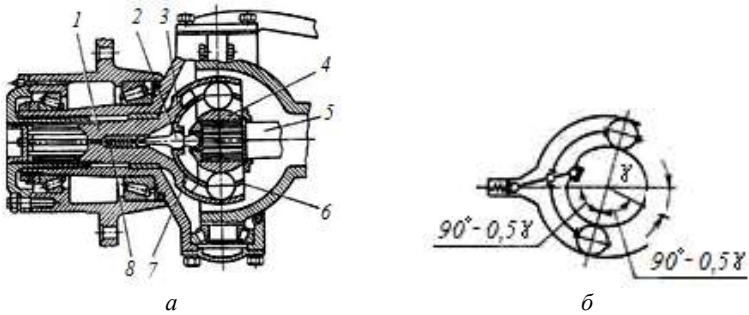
Кульковий карданний шарнір з ділительним важелем (типу «Рцепп»): *a* – установка шарніра в приводі переднього колеса; *б* – схема шарніра; 1, 5 – вал; 2 – ділительний важіль; 3 – сферична чашка; 4 – сферичний кулачок; 6 – сепаратор; 7 – направляюча чашка; 8 – пружина
